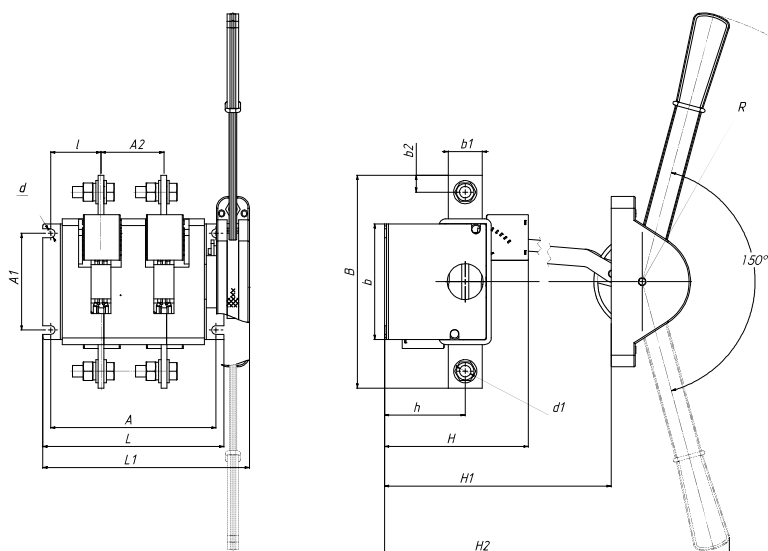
Выключатель-разъединитель на одно направление двухполюсный с передней смещенной ручкой
